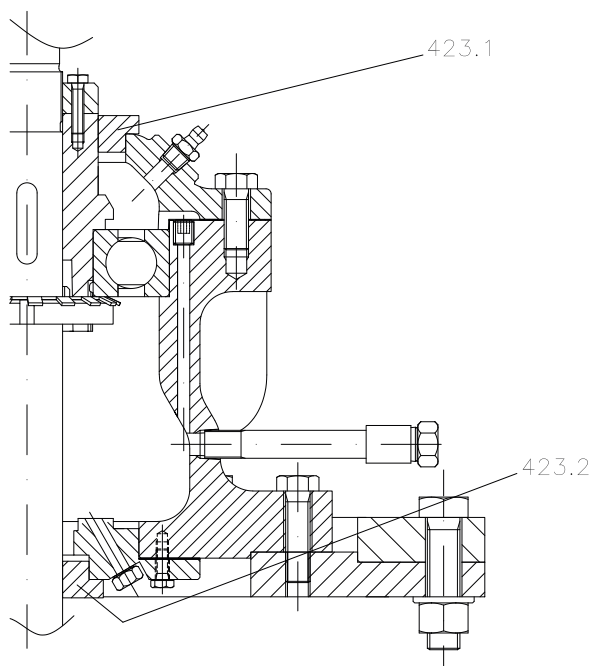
Detail: Lagergehäuse mit fettgeschmiertes Lager und Spritzringe/
